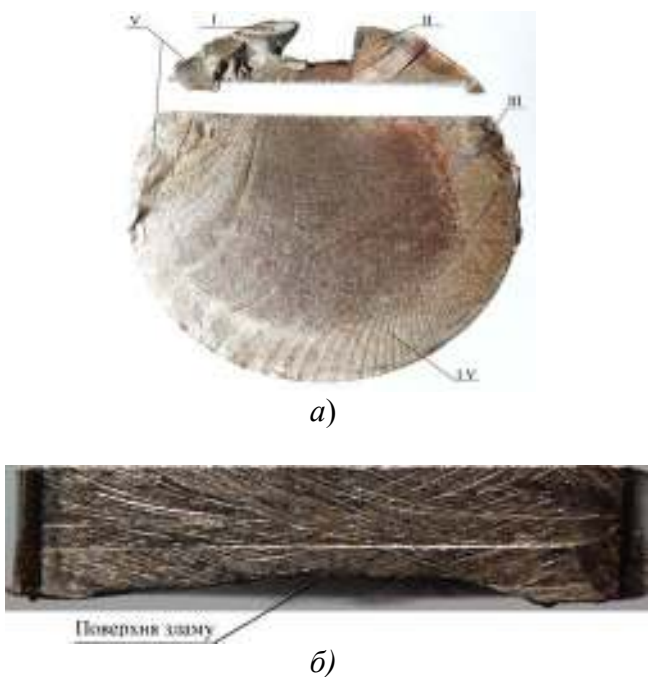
Загальний вигляд зламу хвостовика, де: а - вигляд зверху; б – поперечний перетин форми зламу
